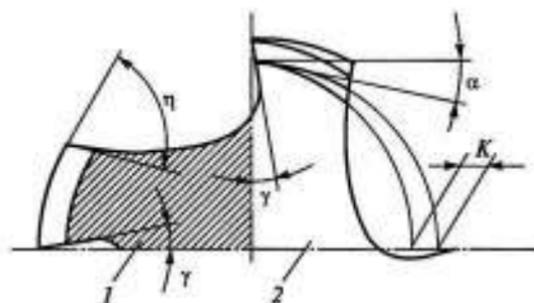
Углы зубьев режущей и направляющей частей метчика:
